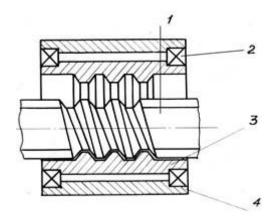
Несоосная передача: 1 — винт; 2- подшипники; 3 — гайка; 4 — корпус
